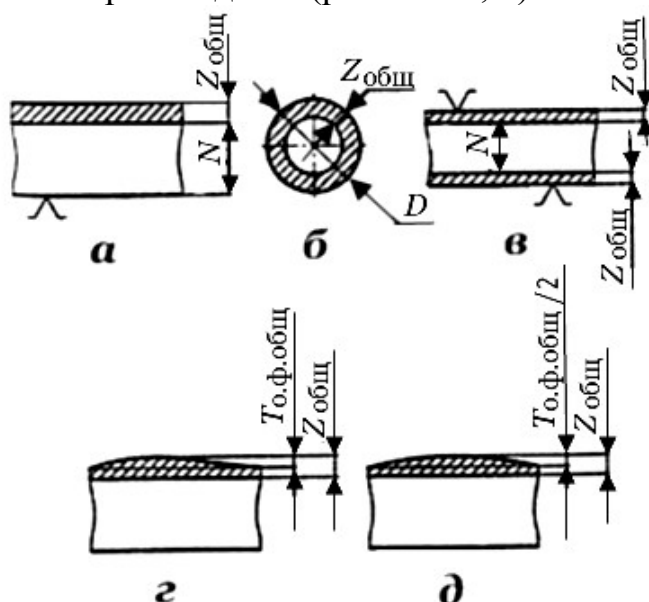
Варианты (а–д) назначения общего допуска для механической обработки: N – номинальный размер; $Z_{общ}$ – припуск на механическую обработку; $T_{o.ф.общ}$ – общий допуск формы поверхности
